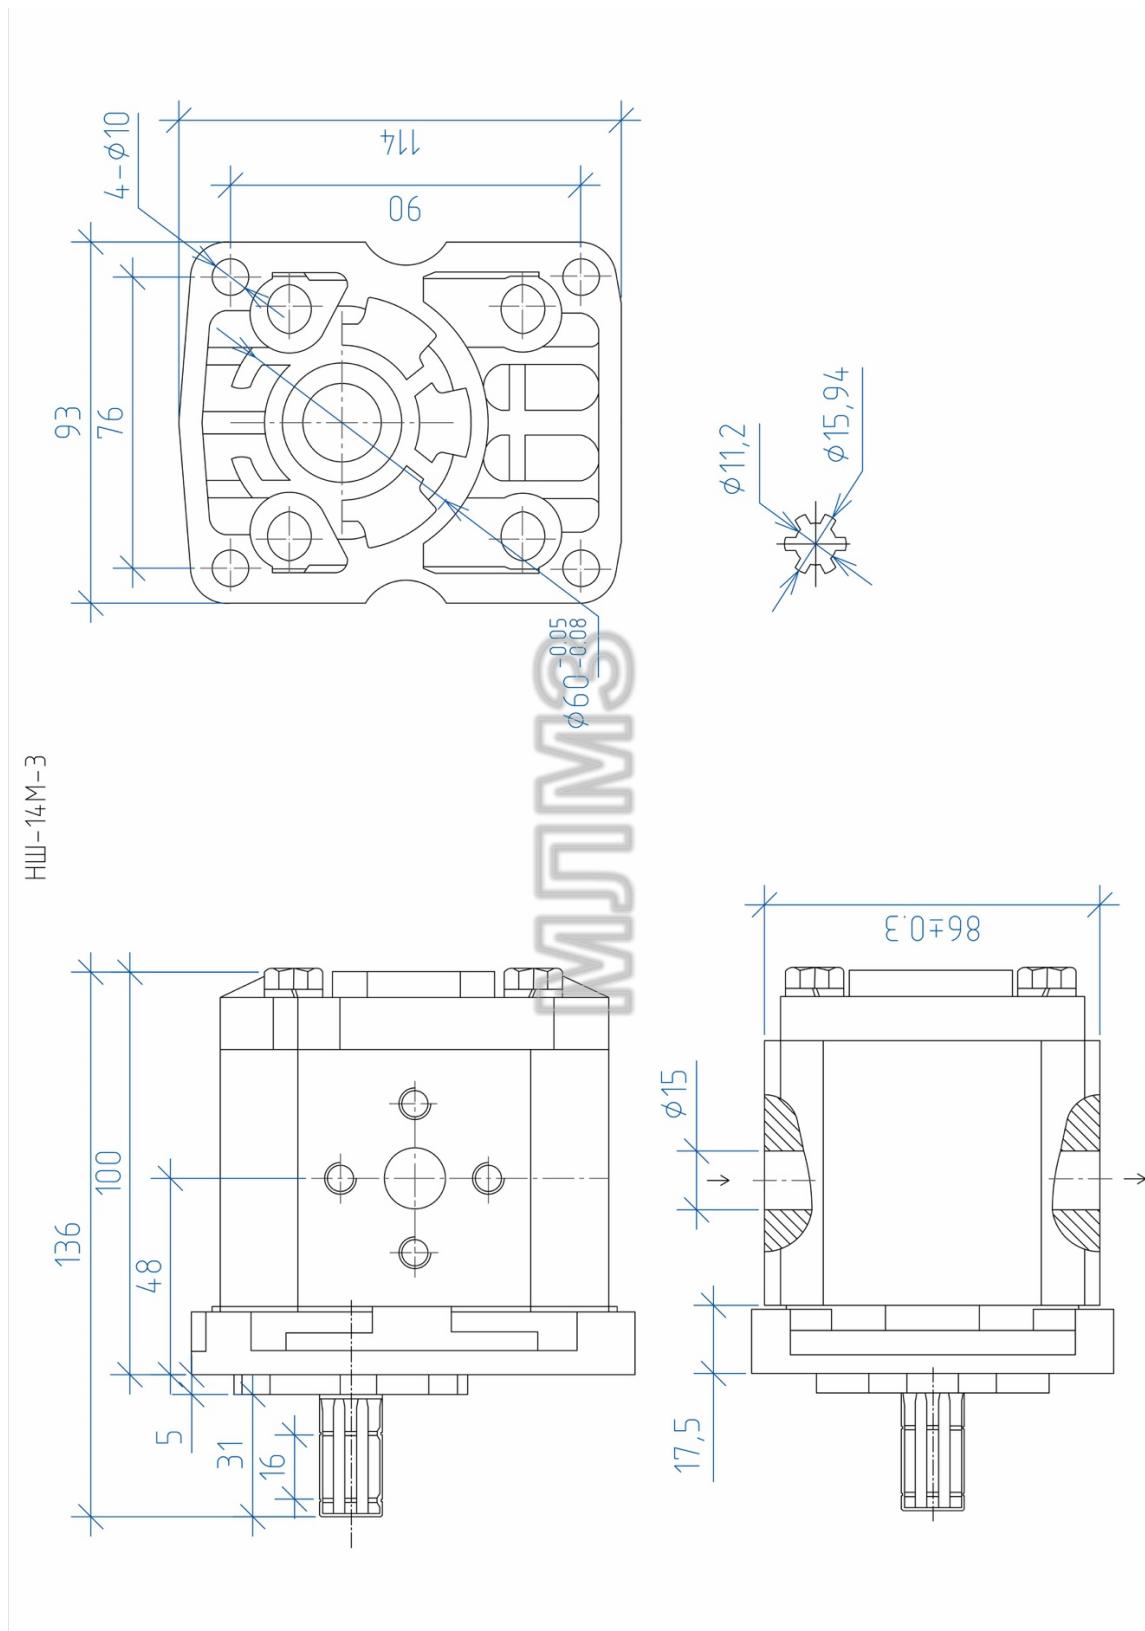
Насосы шестеренные НШ14М-3, НШ14М-3Л. Габаритные и присоединительные размеры.
